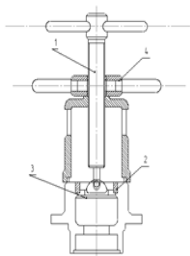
Съемник для выпрессовки подшипников из ступицы колеса с помощью упора
